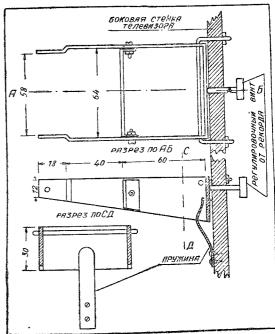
Кронштейн крепления мотора для диска Нипкова с двумя оборотами спирали
